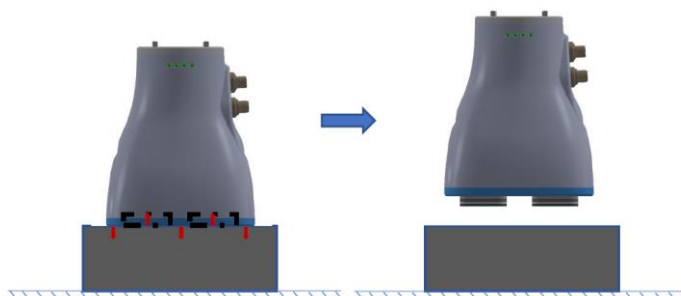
Koncový efektor GECKO GRIPPER [28]
